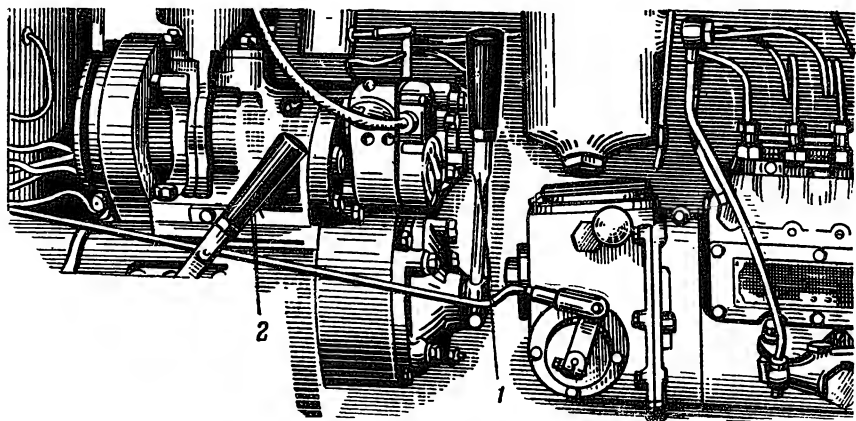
Положение рычагов механизма передачи при запуске пускового двигателя:
